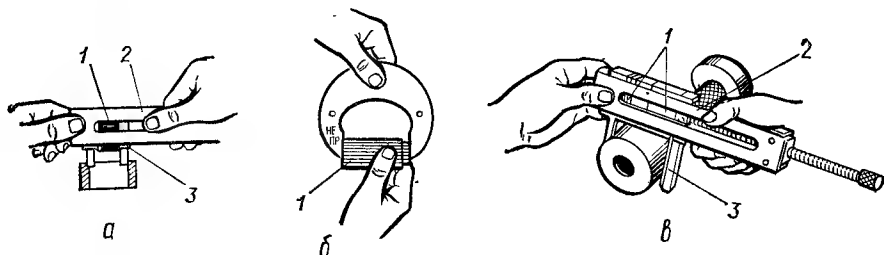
Измерение плоскопараллельными концевыми мерами длины калибра-кольца (а), калибра-скобы (б), калибра-пробки (в):
